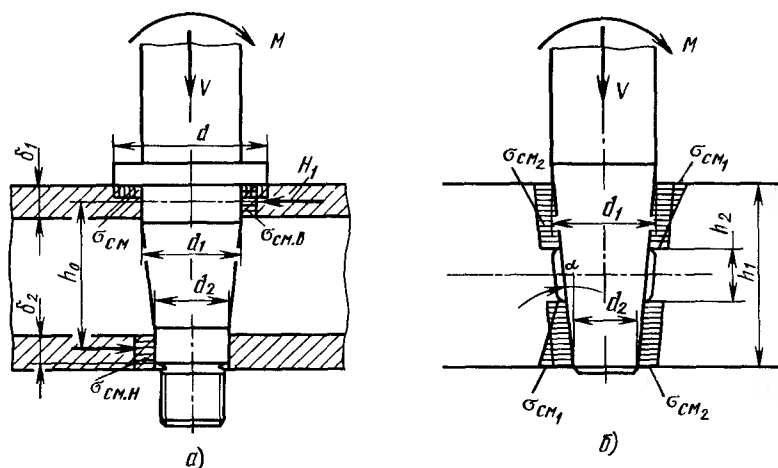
Расчетная схема хвостовика колонны и гнезда плиты:
